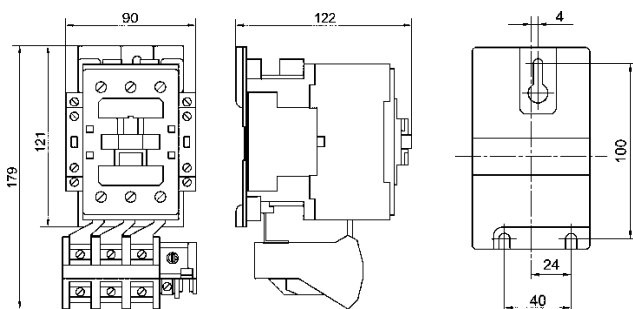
Пускатель нереверсивный ПМ12-063 63А
